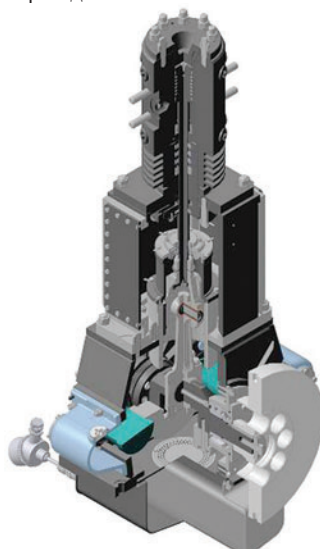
Дожимная компрессорная установка бессмазочная однорядная
